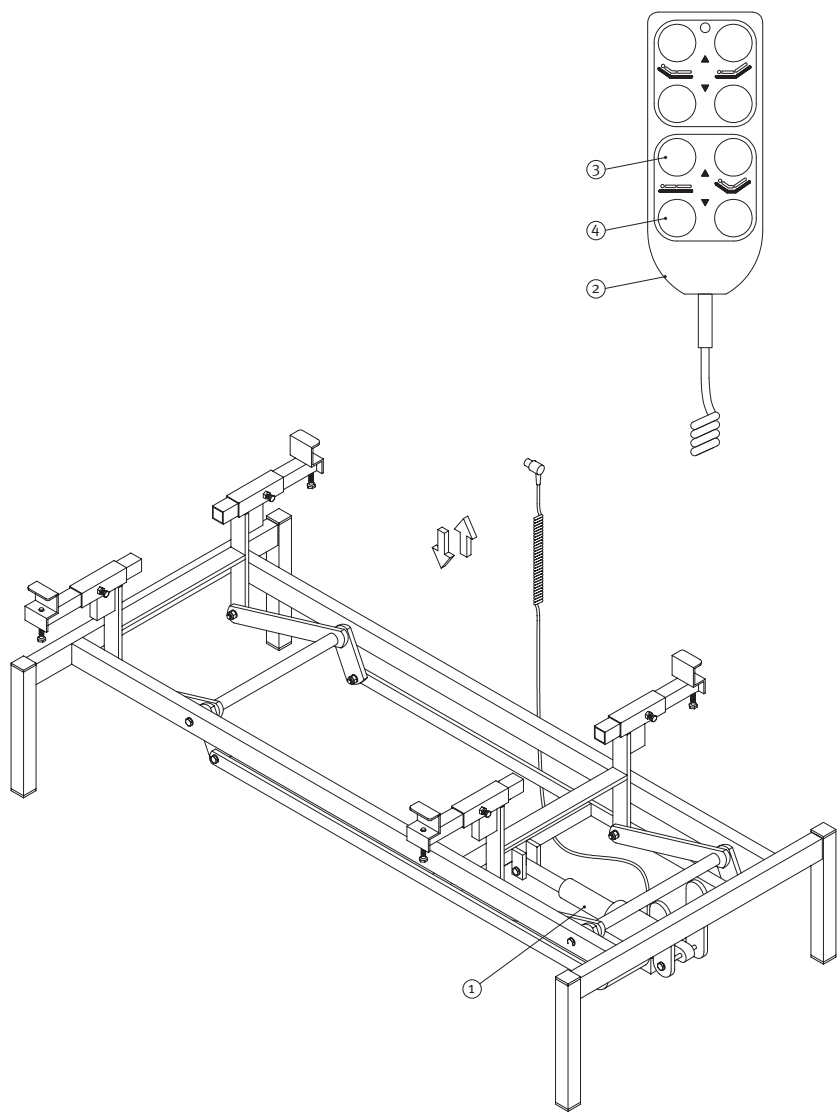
Regolazione verticale del piano rete del letto Art. A 7034/AE.
